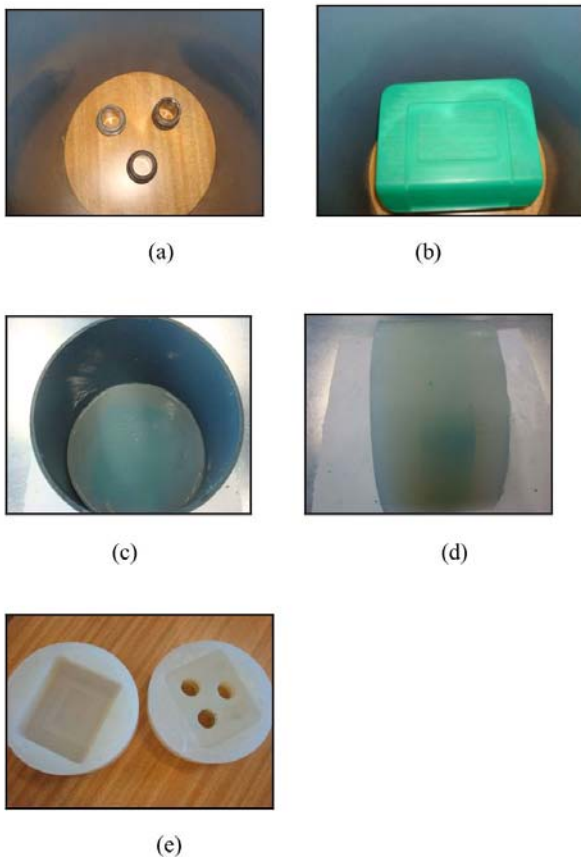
Etapas da fabricação do molde em silicone: (a) estrutura cilíndrica com os parafusos; (b) colocação do protótipo; (c) vazamento do silicone; (d) molde de silicone removido da estrutura cilíndrica; (e) molde em silicone cortado na linha de partição e tendo retirado o protótipo.
